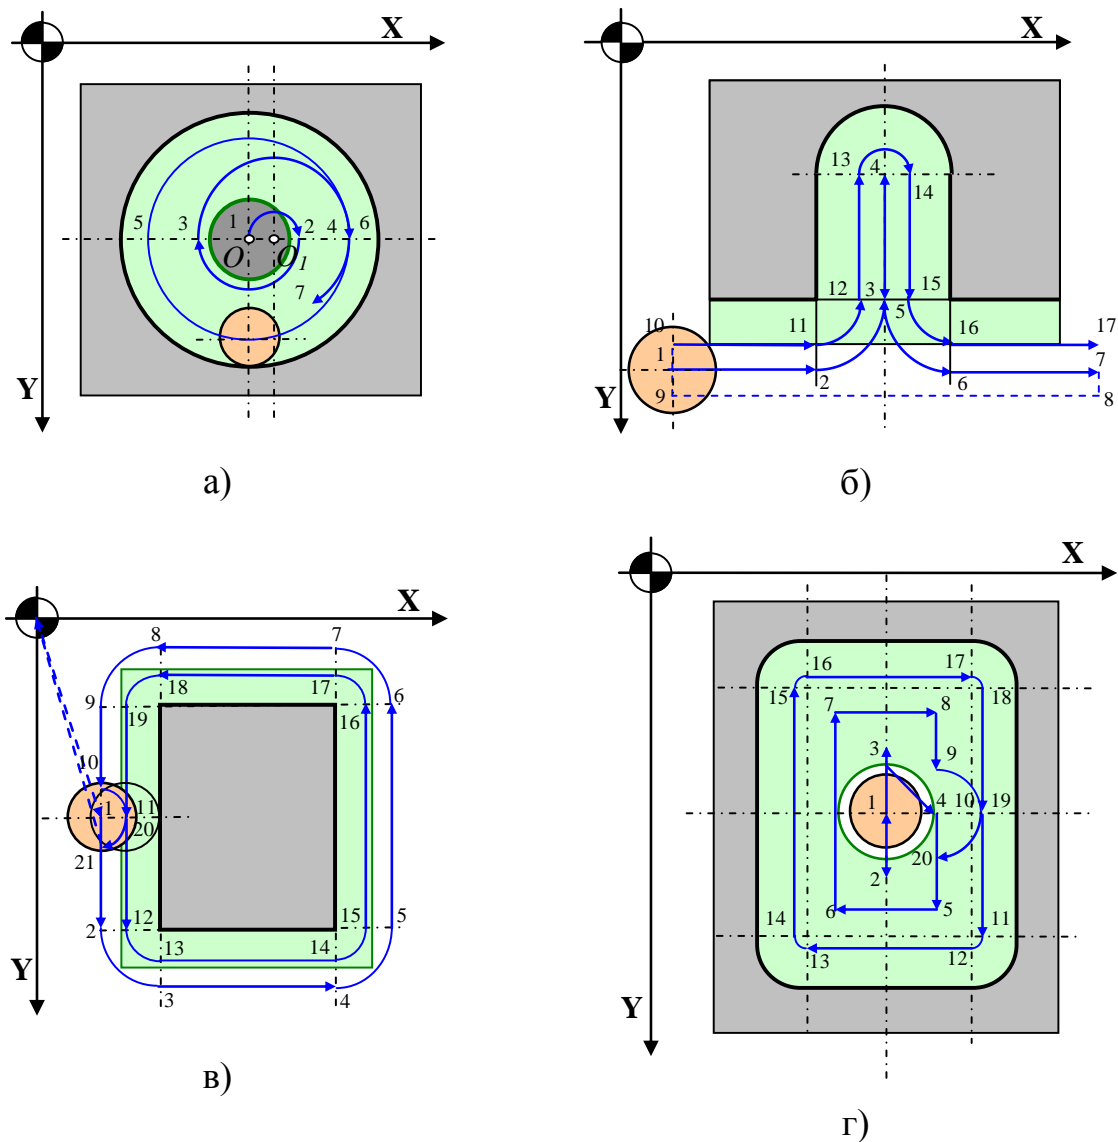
Типовые схемы обработки контуров деталей
